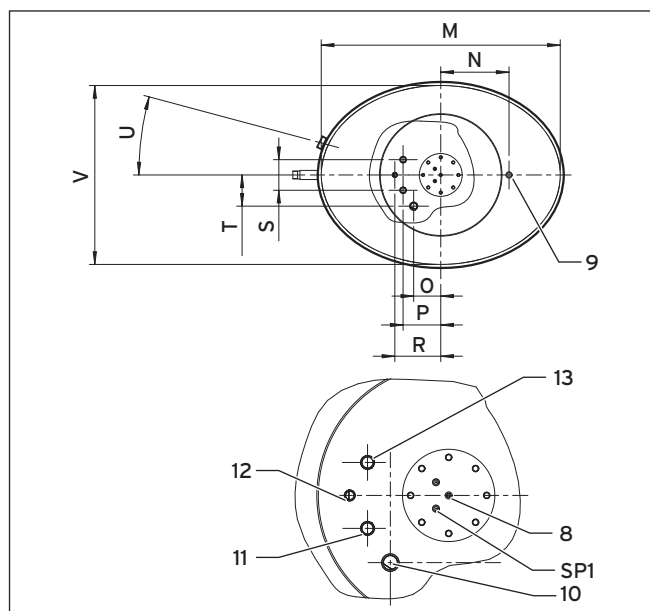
Dimensions de raccordement du ballon combiné auroSTOR VPS SC 1000, vue du dessus
